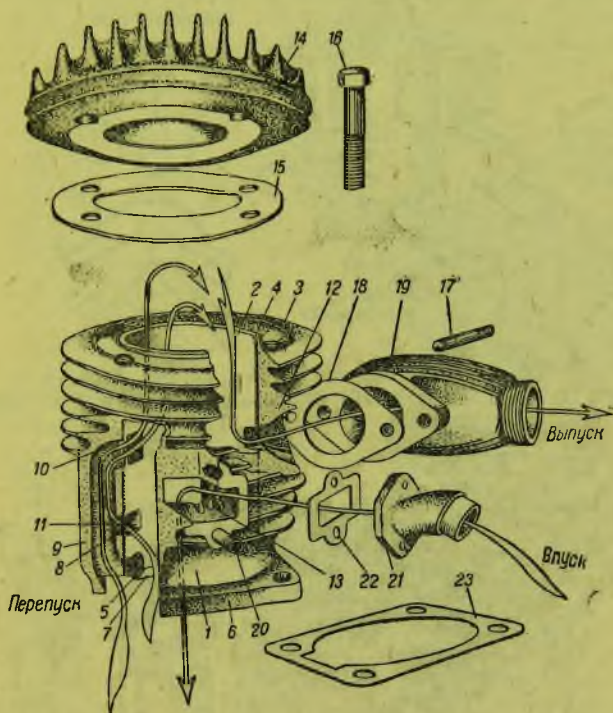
Цилиндр двигателя ИЖ-7 и Л-300
